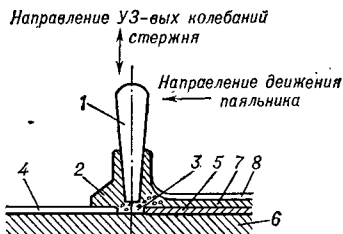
Схема действия ультразвукового паяльника: 1 — стержень паяльника; 2 — расплавленный припой; 3 — место контакта расплавленного припоя с чистым металлом; 4 — окисная плёнка; 5 — слой, представляющий собой смесь припоя с чистым металлом; 6 — чистый металл; 7 — затвердевший слой; 8 — остатки окислов на поверхности припоя.
